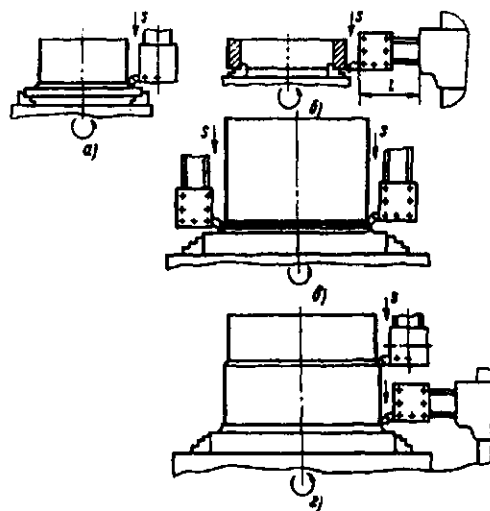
Схемы обтачивания цилиндрических поверхностей
